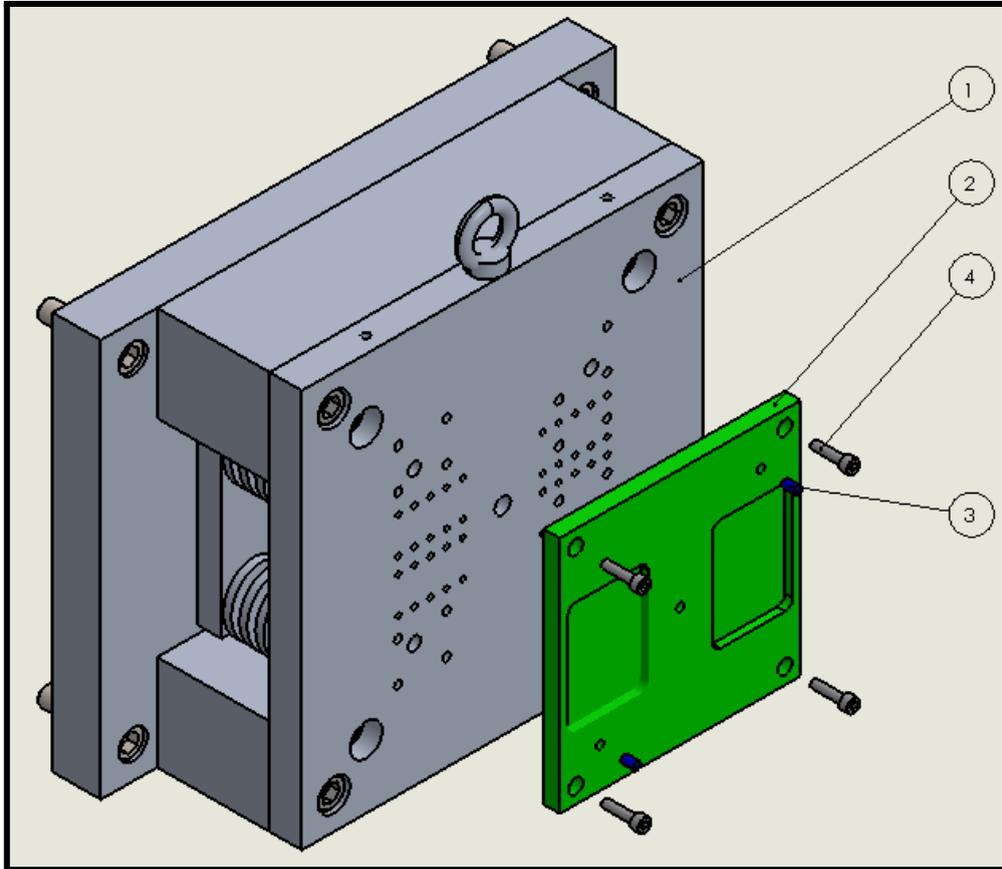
M. Vista explosionada de la configuración 1 del portamolde
